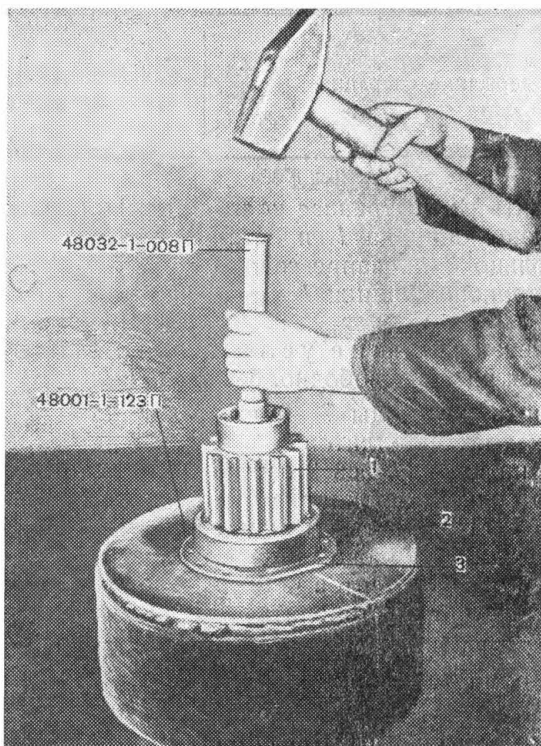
Спрессовка шестерни подшипника и крышки с несущего диска:
